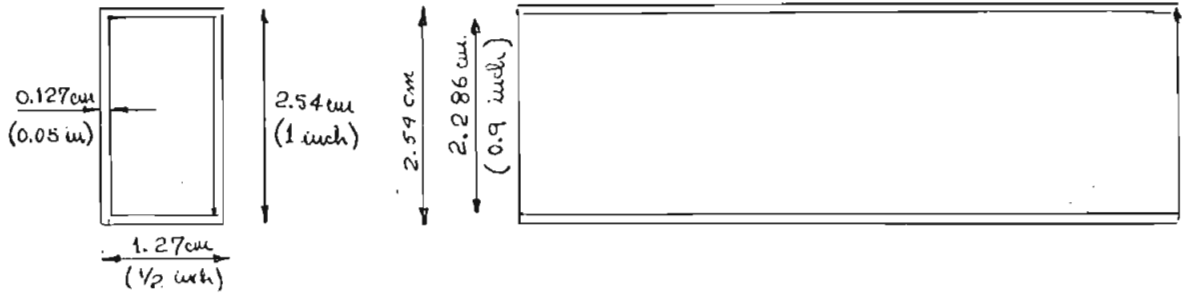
Dimensiones geométricas de la guía WR-90
